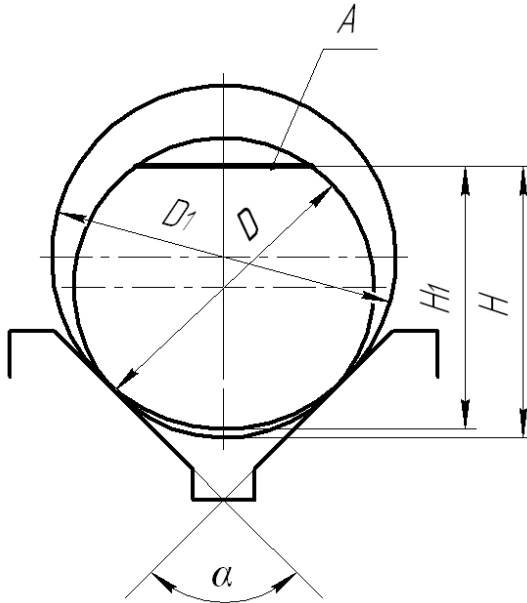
Схема впливу діаметра базової поверхні заготовки на величину виконуваного розміру
